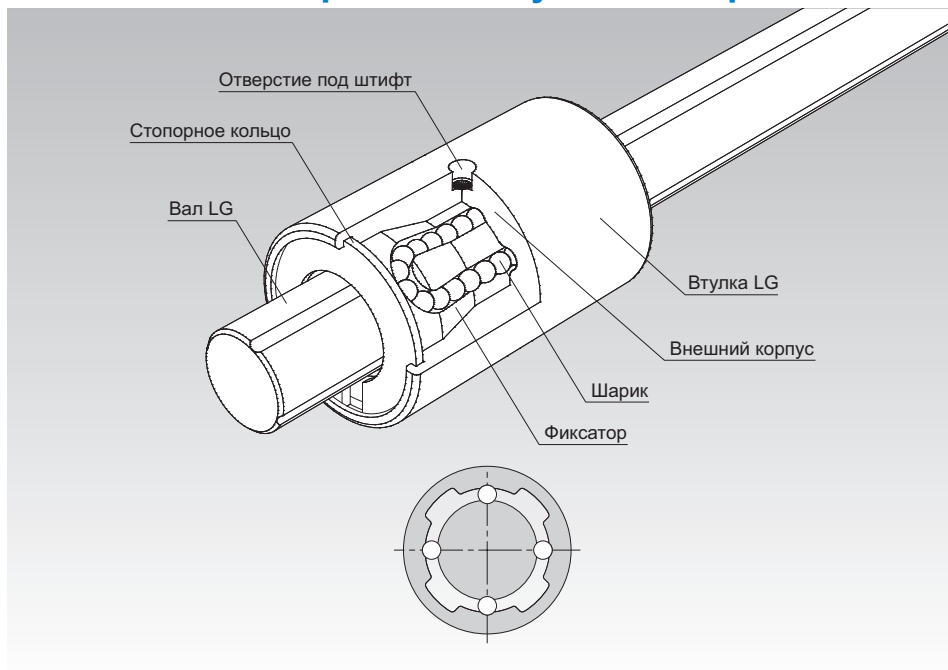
Конструкция шариковой втулки с направляющей модели LG
